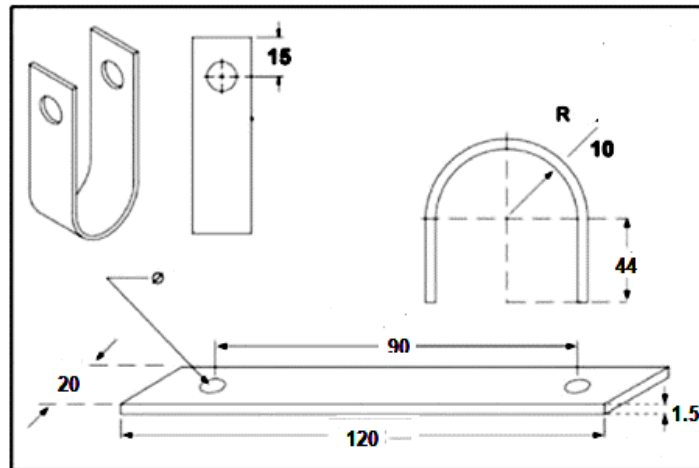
Forme et dimensions de l'éprouvette U-BEND
